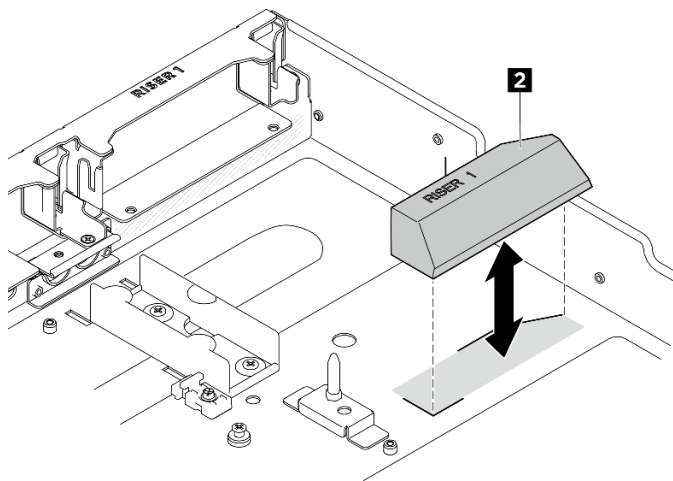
Installieren der DPU-Luftführung am Gehäuse
